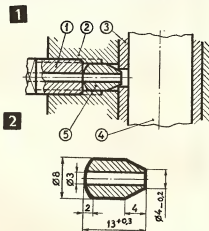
Узел в сборе: 1 — масленка; 2 — корпус распределителя; 3 — подшипник; 4 — валик распределителя; 5 — цилиндрический клин.
